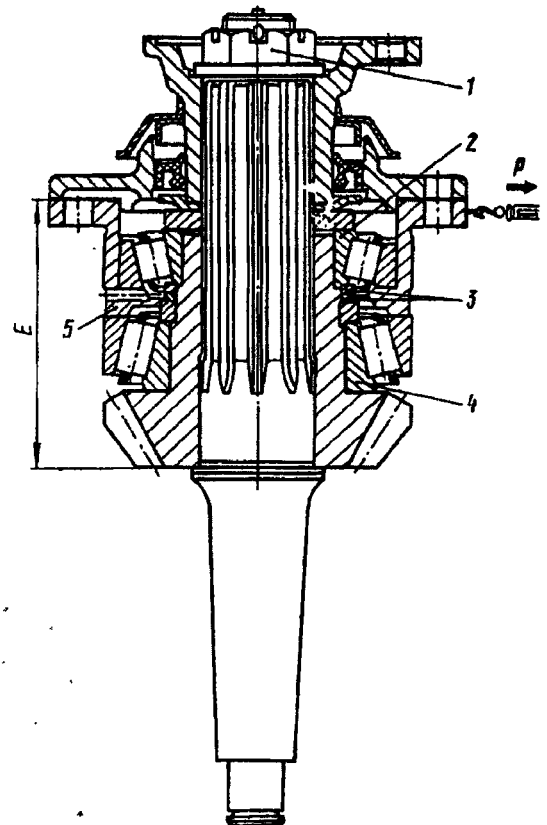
Регулирование подшипников ведущего конического зубчатого колеса:
